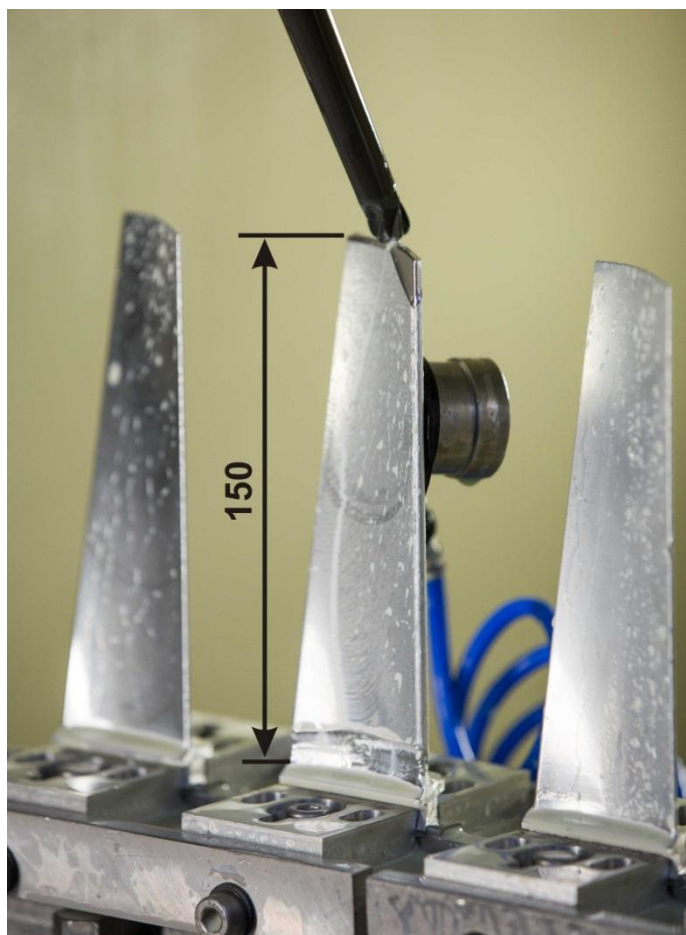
Обработка лопатки с закреплением только за один край (замок) и установкой гасителя вибраций на свободный конец лопатки
